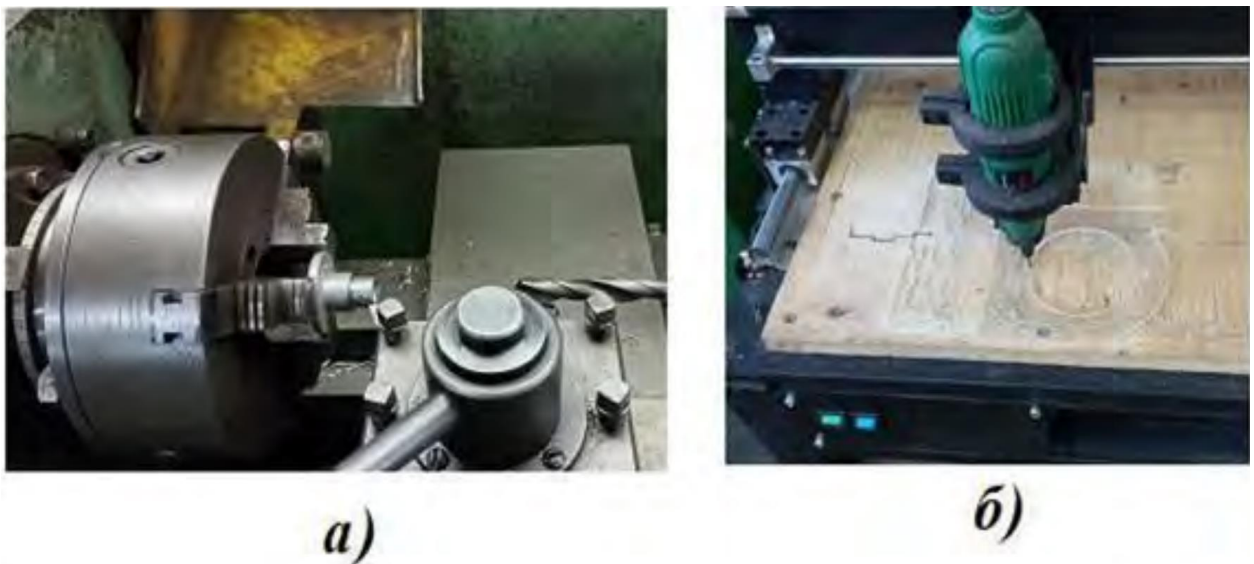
Виготовлення деталей корпусу моделі дробарки: а) токарні роботи на верстаті; б) фрезерні роботи на верстаті з ЧПУ.
